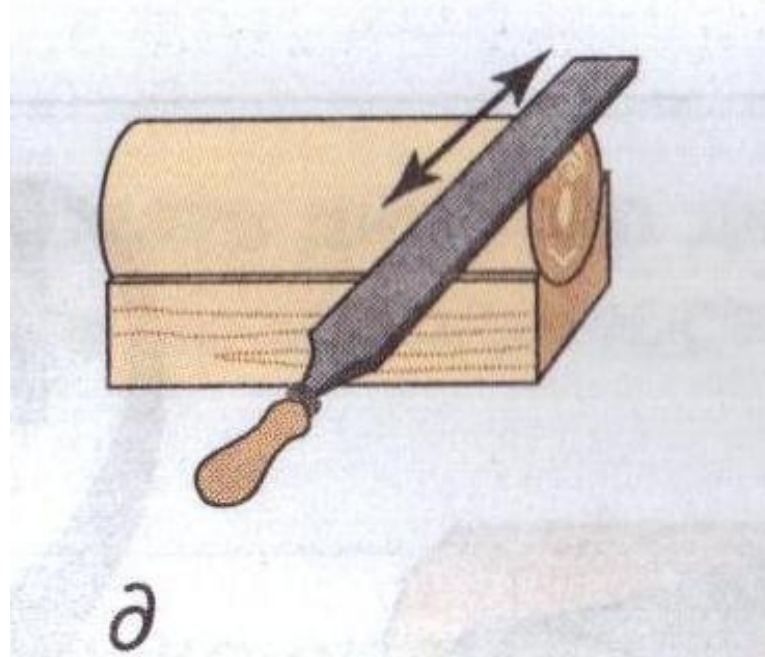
Последовательность изготовления детали цилиндрической формы ручным инструментом.
